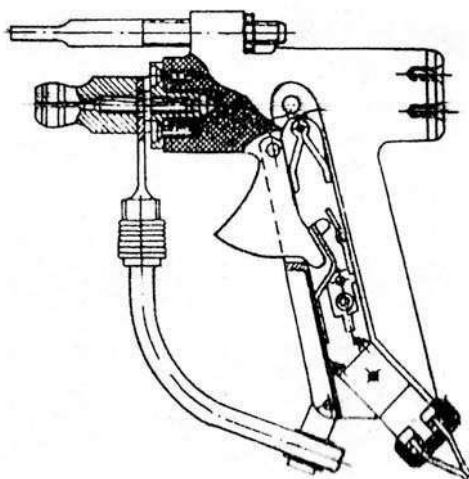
Пистолет для ручной приварки шипов под флюсом
